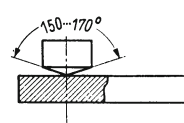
Gedrehter Kegelsbuckel, z. B. Anschweißen eines Zapfens an einen Flacheisenhebel.
